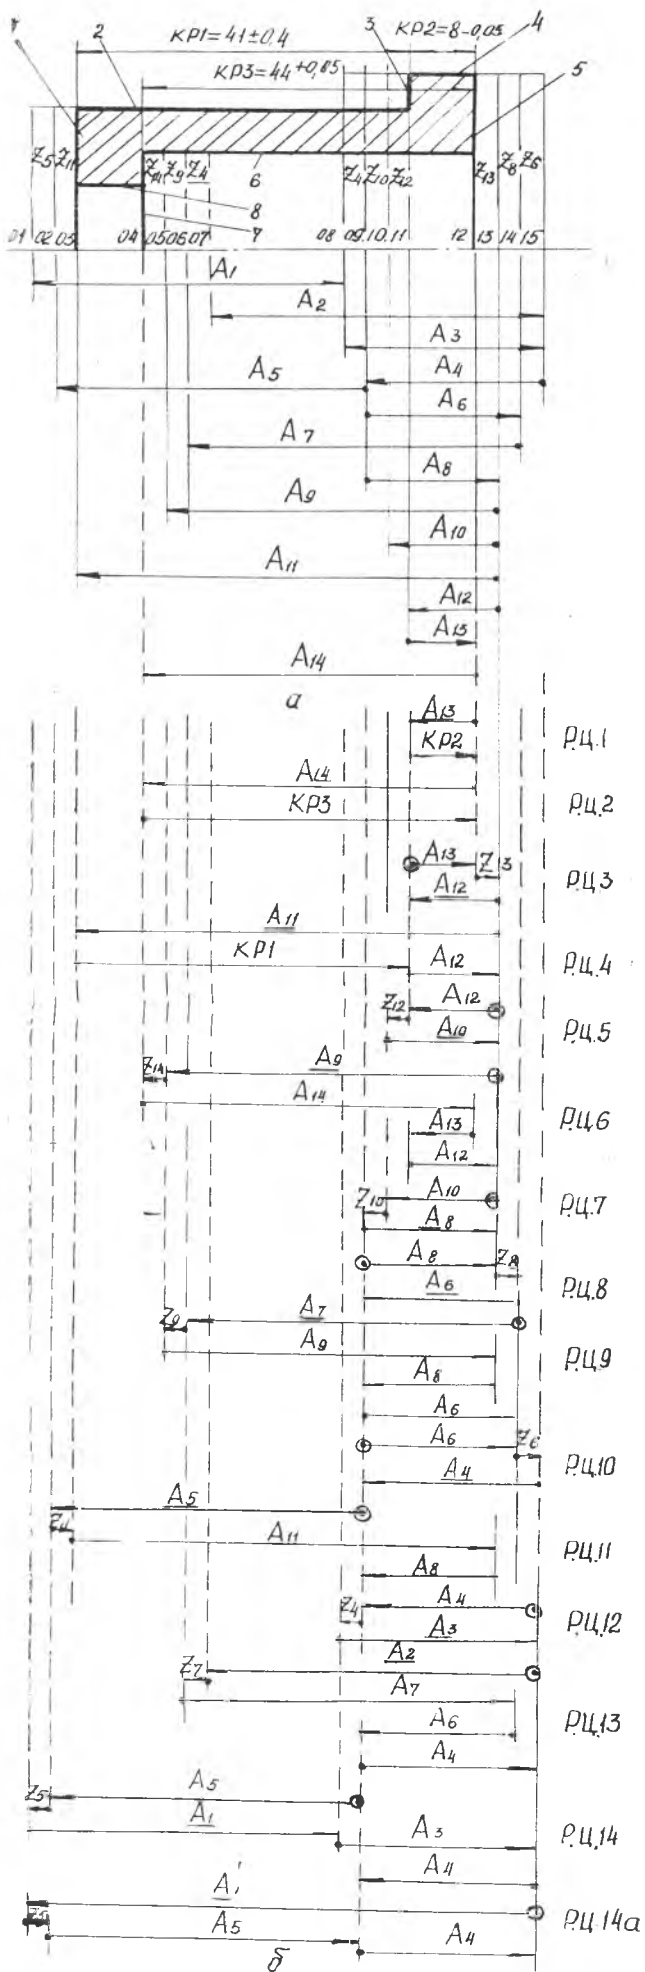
Размерная схема ТП обработки обоймы подшипника (а) и размерные цепи (б)
